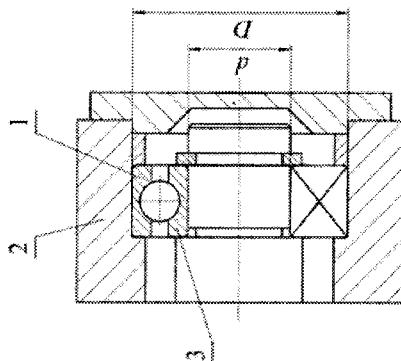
Радиальный шариковый подшипник качения: 1 — наружное кольцо подшипника; 2 — корпус механизма; 3 — внутреннее кольцо подшипника
